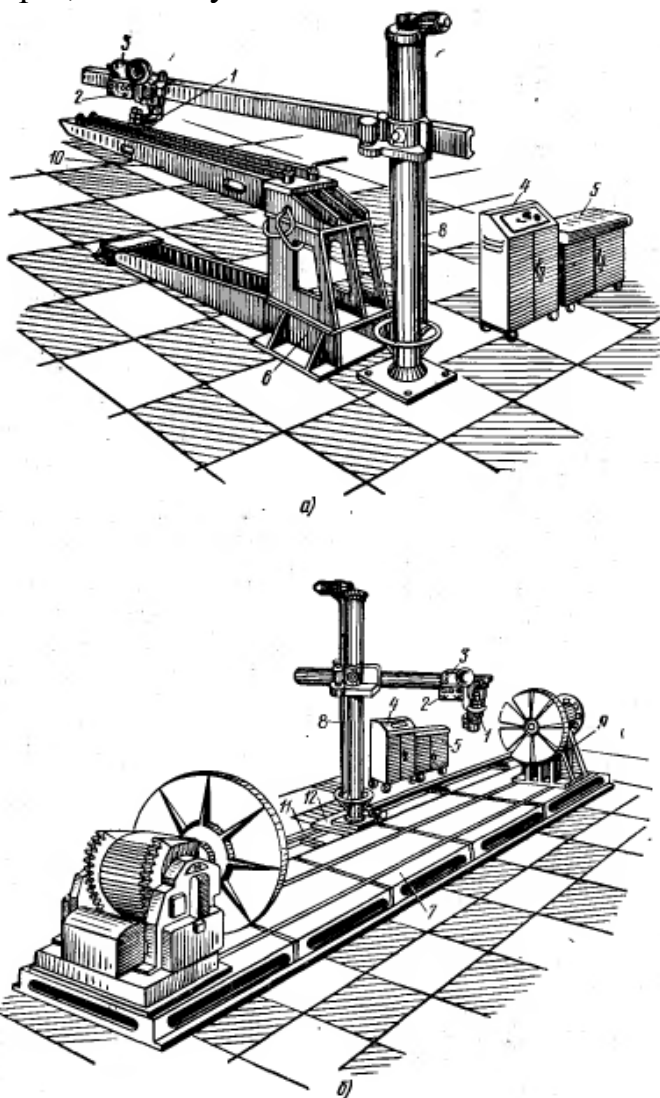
Типовые компоновки для сварки:
